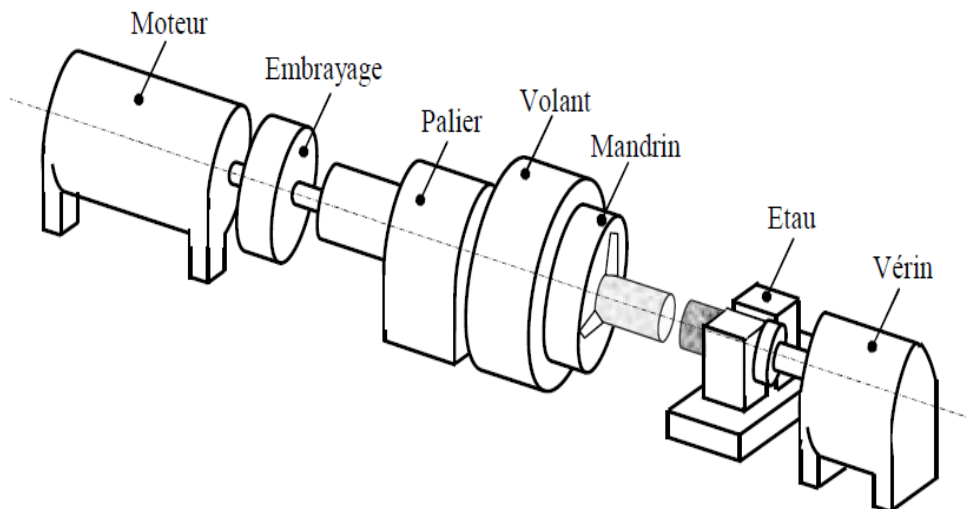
Séquences du soudage par friction inertielle [22].
